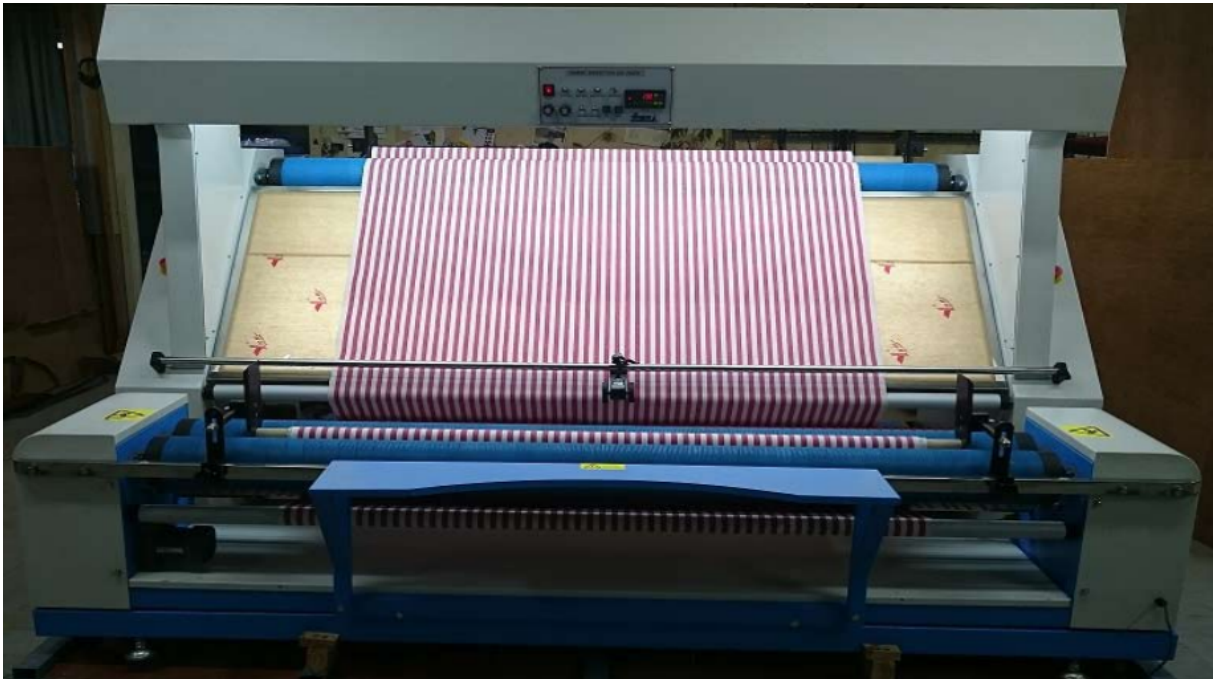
Máquina de inspeção Retirado de: (Svegea 2015)
